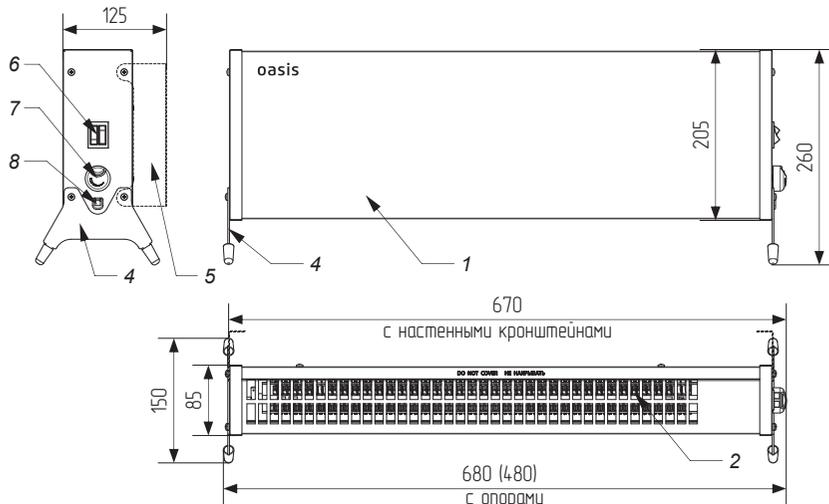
Габаритный чертеж и элементы конструкции электрического обогревателя.
